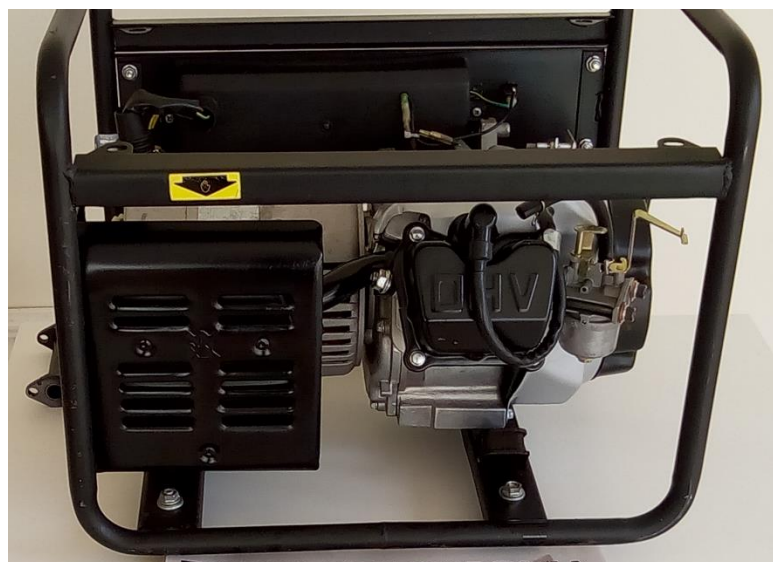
Aspecto final da montagem do conjunto do cabeçote do GMG.
